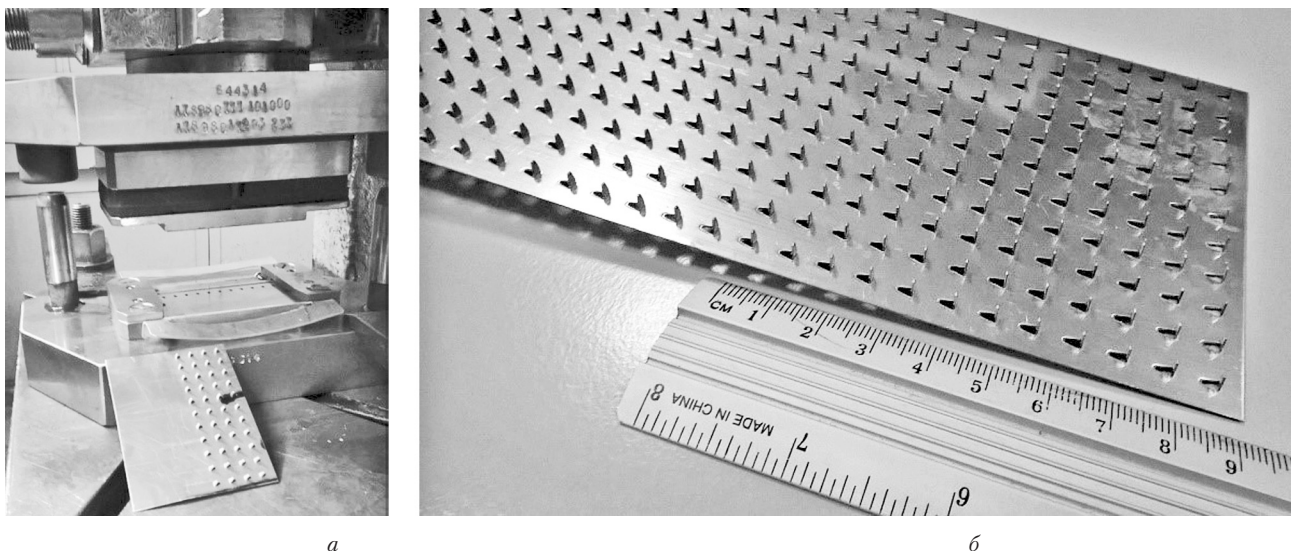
Штамп для изготовления зубчатых накладок (а) и полученная заготовка (б)
